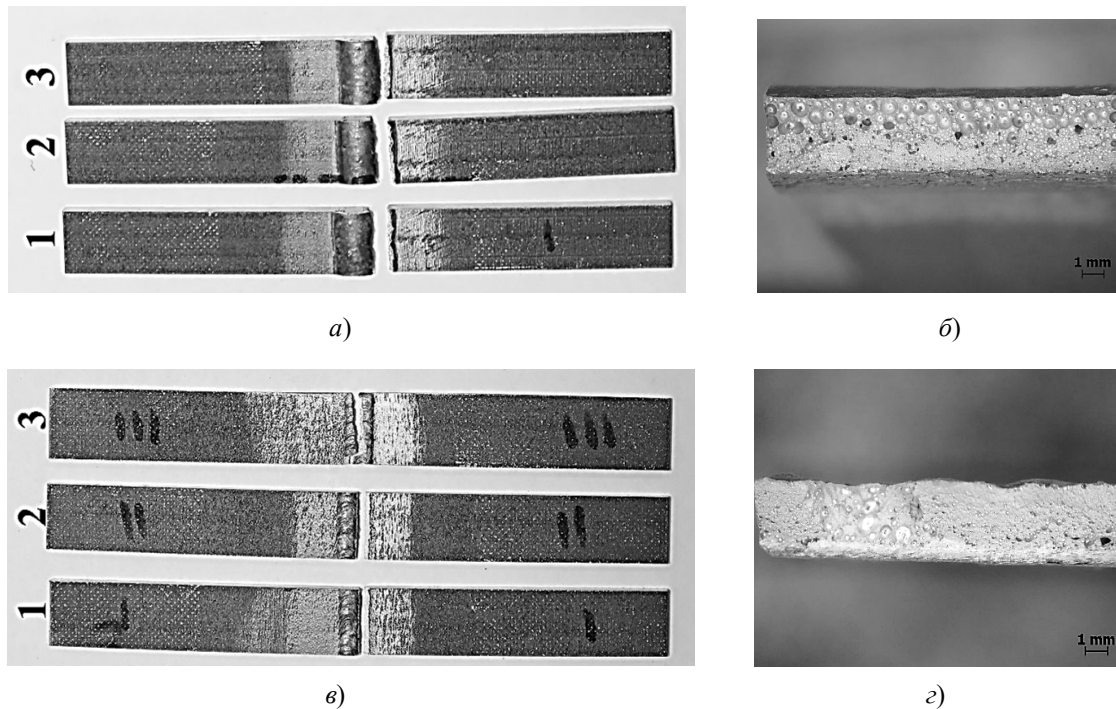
Разрушение образцов сварных соединений при испытаниях на статическое растяжение (а, в) и поверхность излома (б, г):
